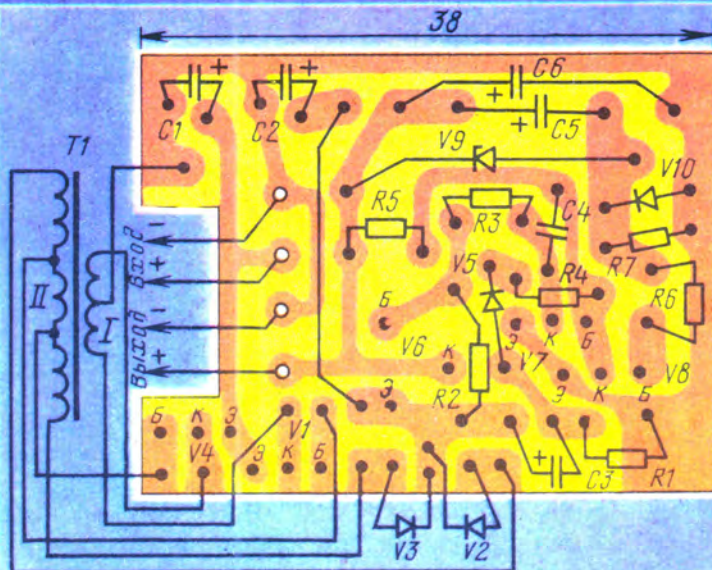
Чертеж печатной платы и схема соединений модульного блока с преобразователем
